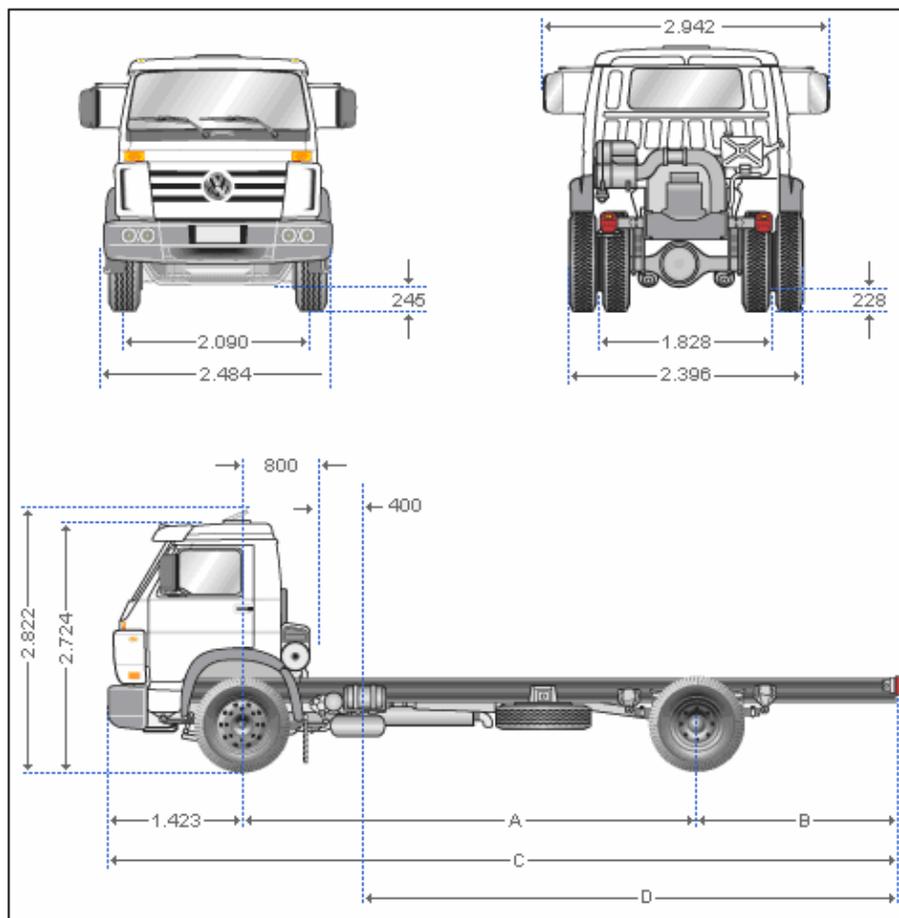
Vistas frontal, traseira e lateral, com dimensões em milímetros, do caminhão T13
